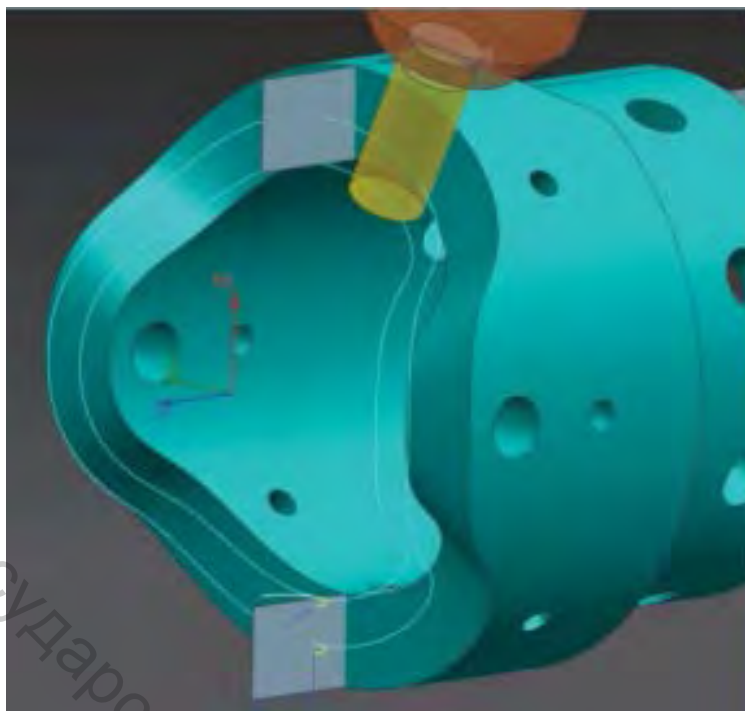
Траектория инструмента при чистовой фрезерной обработке фасонной поверхности
